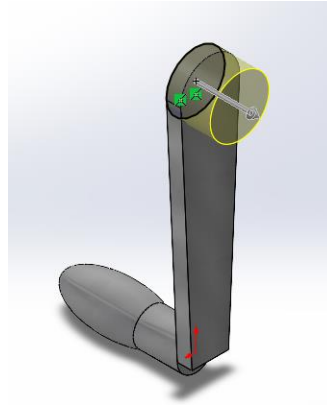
Extrusión del pivote de la manivela en SolidWorks.
